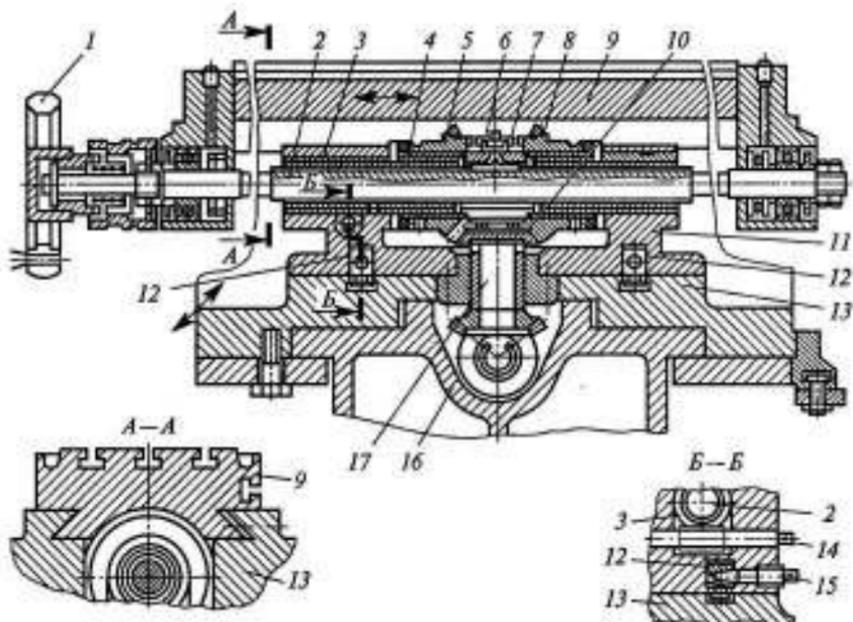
Стол универсального консольно-фрезерного станка:
